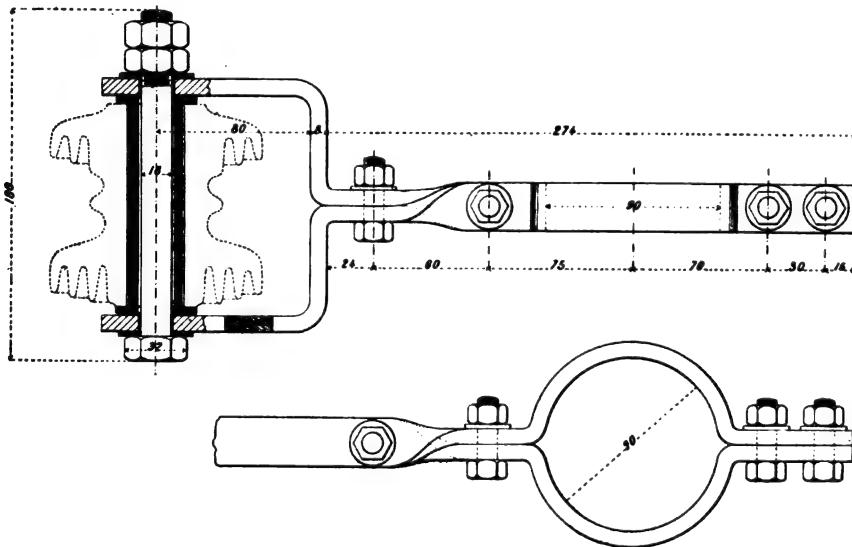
Support spécial pour isolateur d'arrêt placé sur un poteau.
